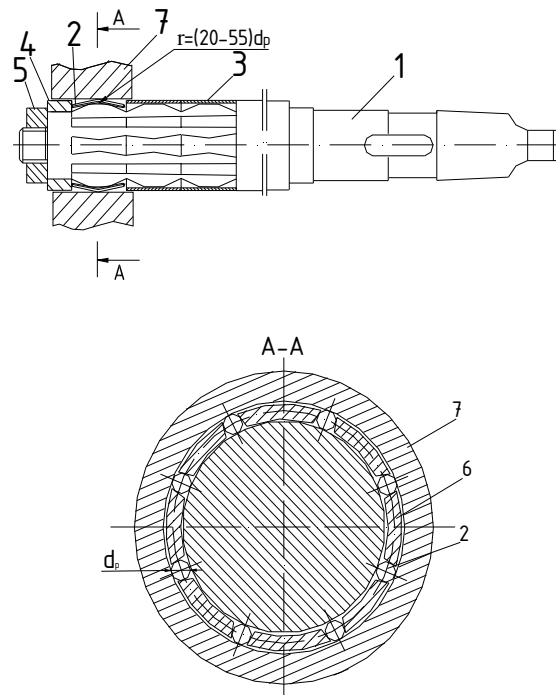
Устройство для ударного чистового раскатывания отверстий
